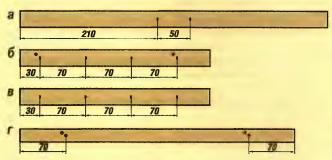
Разметка отверстий в деталях рамки: а— верхний брусок (470х25х13 мм); б— условно-левая планка (290х25х9 мм); в— условно-правая планка; г— нижний брусок (420х20х10 мм)
